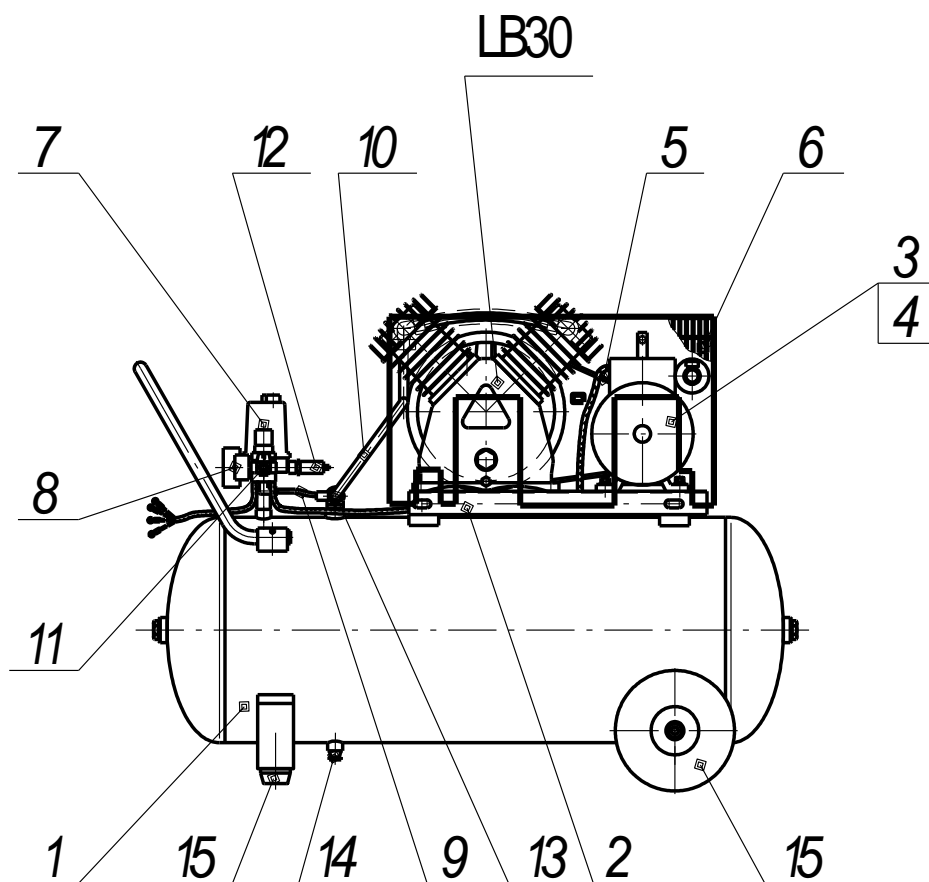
Общий вид компрессора СБ4/С-100.LB30, СБ4/С-100.LB30А
